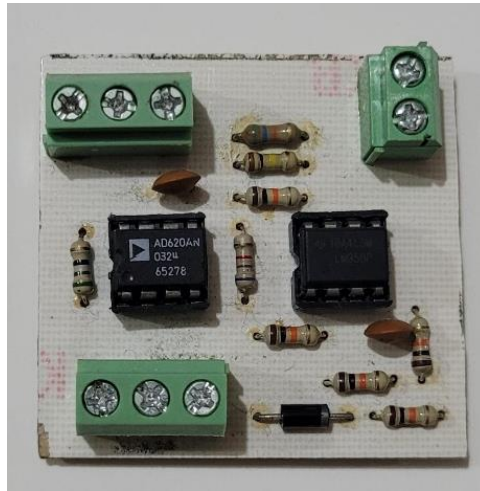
Circuito en PCB del Sensor EMGs para la medición de un grupo muscular.
